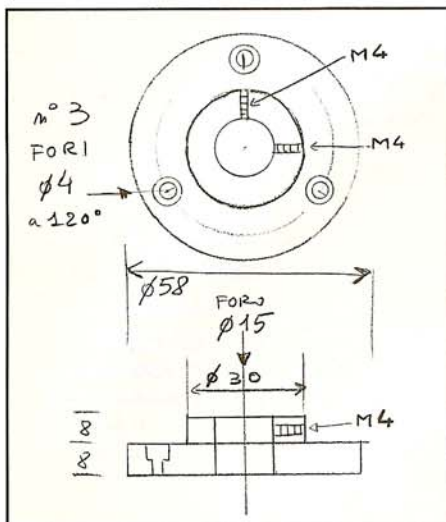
La base in anticorodal per il fissaggio sul giradischi.
